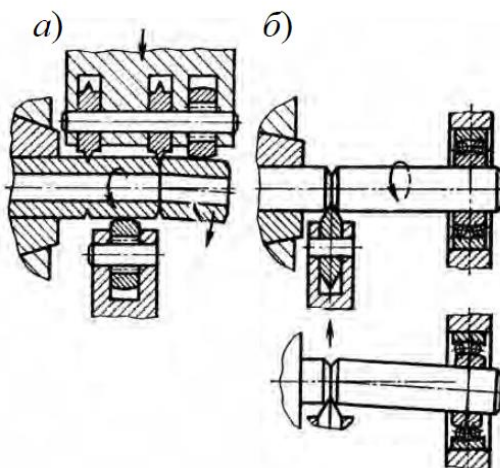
Схема разделения круглого проката и труб на заготовки: а – обкатка клиновым роликом; б – обкатка и разрушение
